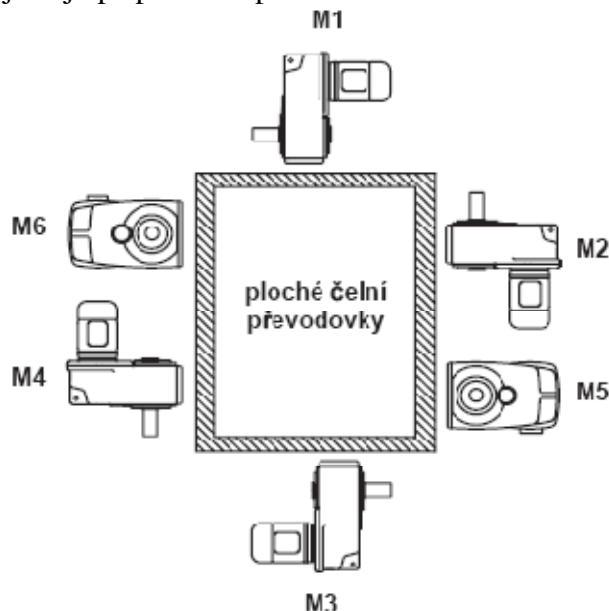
Zvolena převodovka SK 8382/42 AFG [2]
